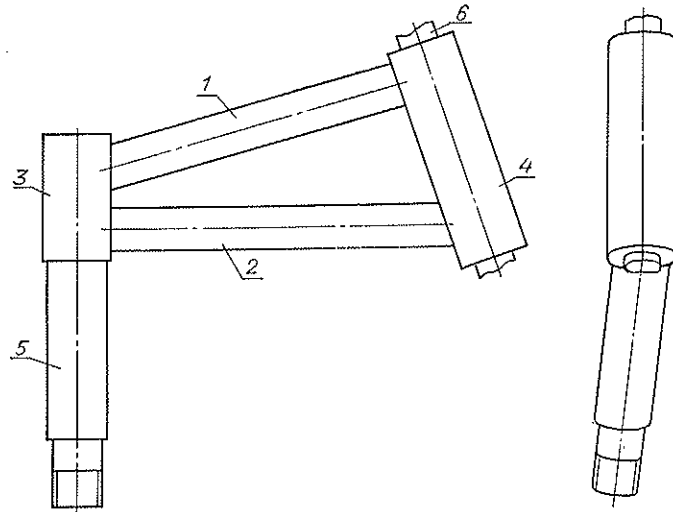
Общий вид маятника без усилительной пластины. (Назначение деталей 1—6 дано на рис. 65).
